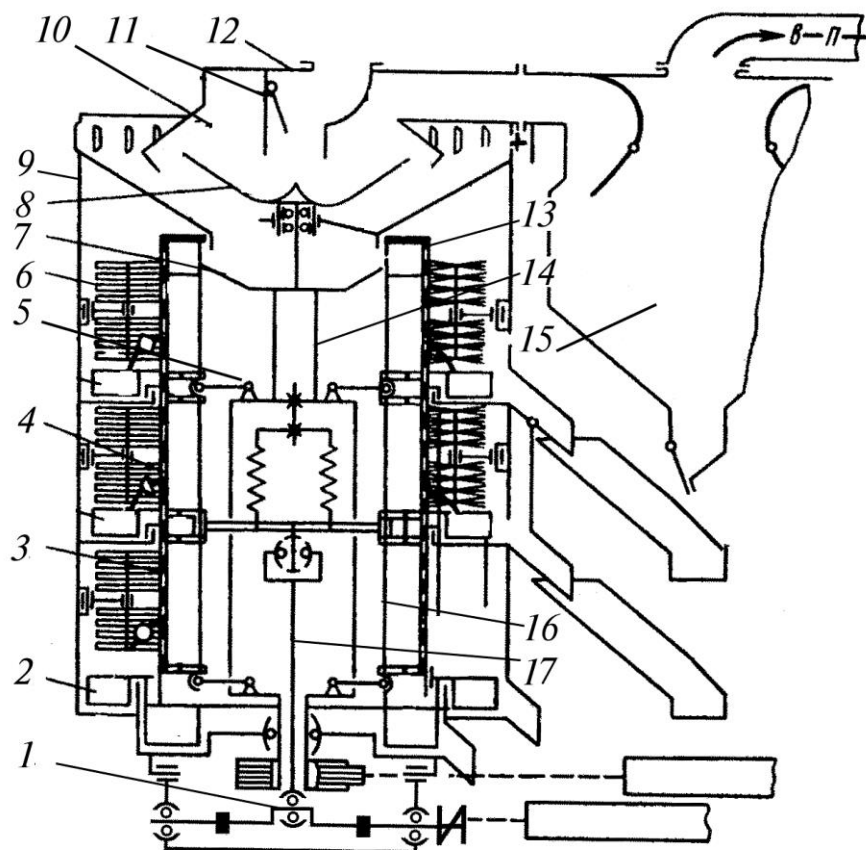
Конструктивная схема одного блока виброцентробежного сепаратора А1-БЦСМ-100: 1 – вибровозбудитель; 2 – скребки; 3 – решето зерновое; 4 – решето сортировальное; 5 – подвески; 6 – очистители; 7, 8 – разбрасыватели дисковый и конический; 9 – корпус; 10 – канал аспирационный; 11 – клапан; 12 – дозатор; 13 – решето подсевное; 14 – ротор; 15 – камера осадочная; 16 – барабан решетный; 17 – шатун
